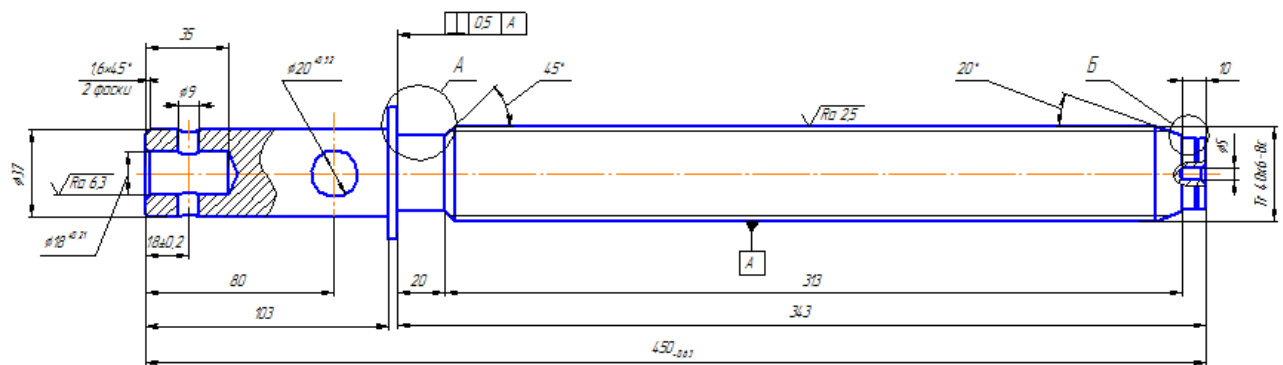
Загальний вигляд деталі «Гвинт опори»
